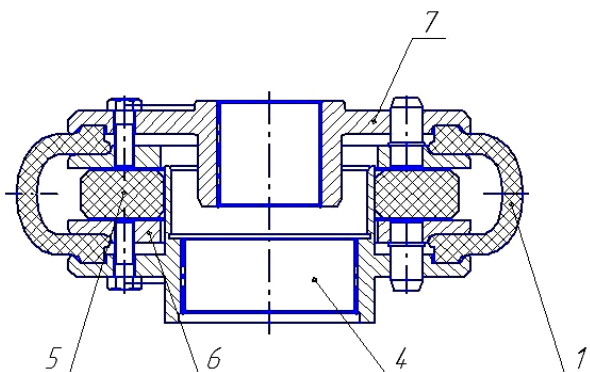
Муфта шинно-зубчатая: 1 - оболочка высокоэластичная; 4 - полумуфта зубчатая; 5 - прокладка; 6 - полукольцо; 7 – полумуфта
